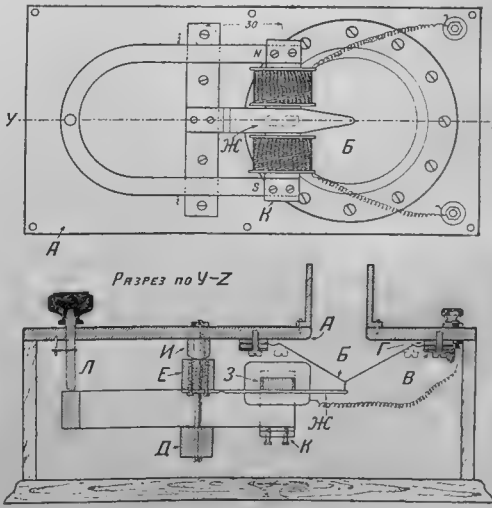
Вид сверху и разрез готового громкоговорителя.
